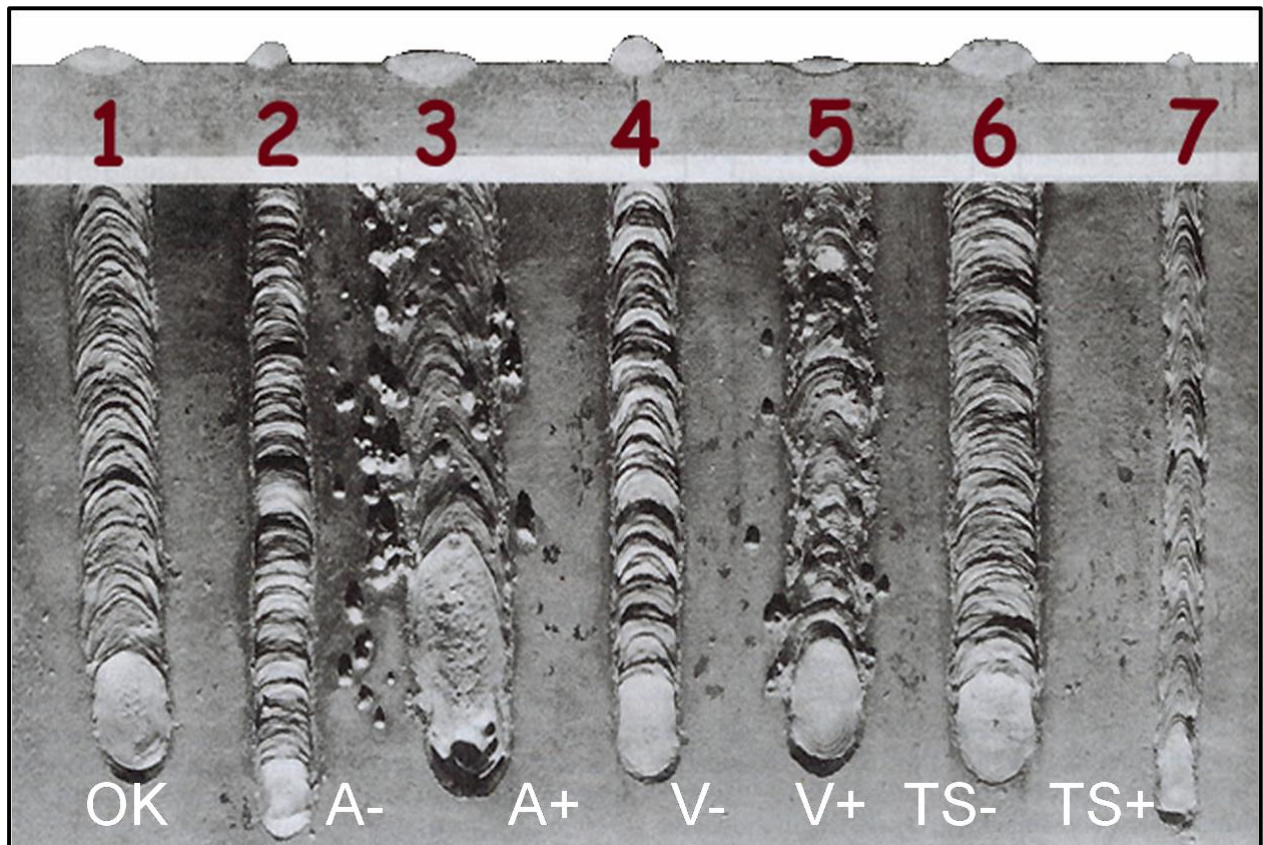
Efecto de los principales parámetros de soldeo en el cordón. Fuente: CESOL
